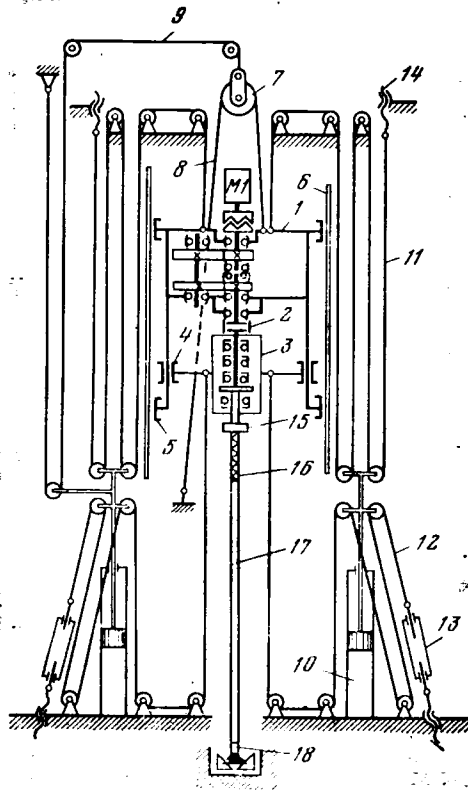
Кинематическая схема вращательно-подающего механизма шпиндельного типа станка шарошечного бурения СБШ-250МНА-32 с канатно-поршневой подачей
